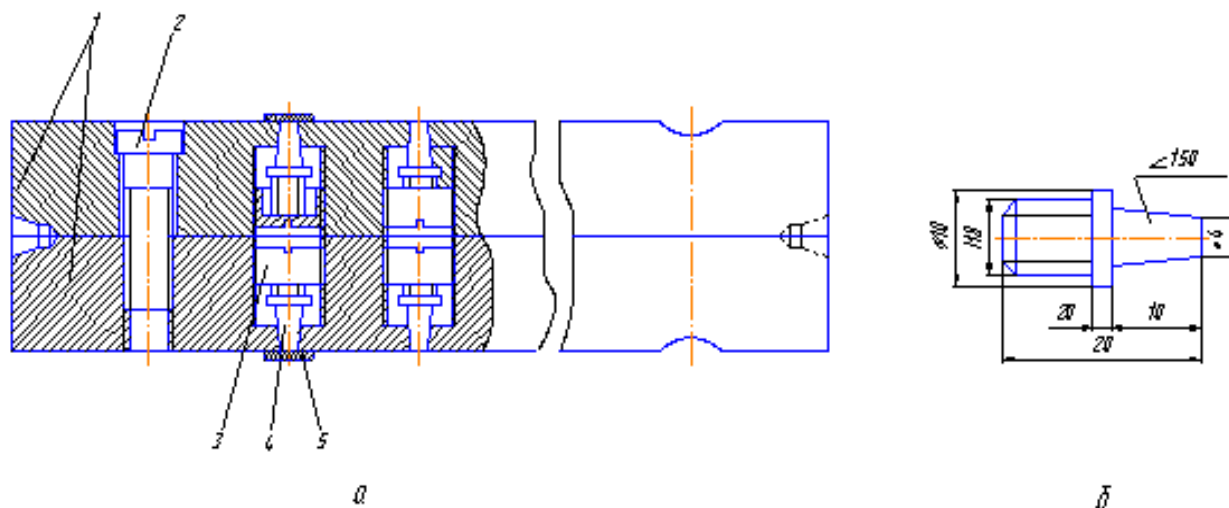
Разборный блок образцов для наплавки (а) и форма штифта (б):
